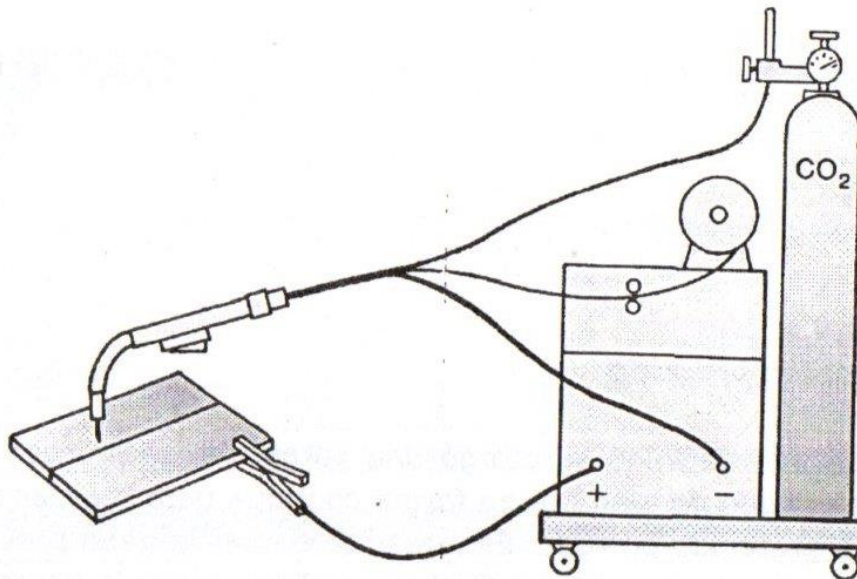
Esquema básico de un equipo para soldadura MIG
